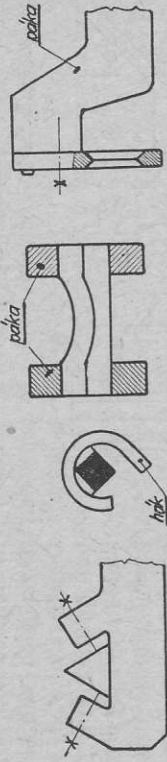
Obr. 312. Obr. 313. Obr. 314. Obr. 315.
